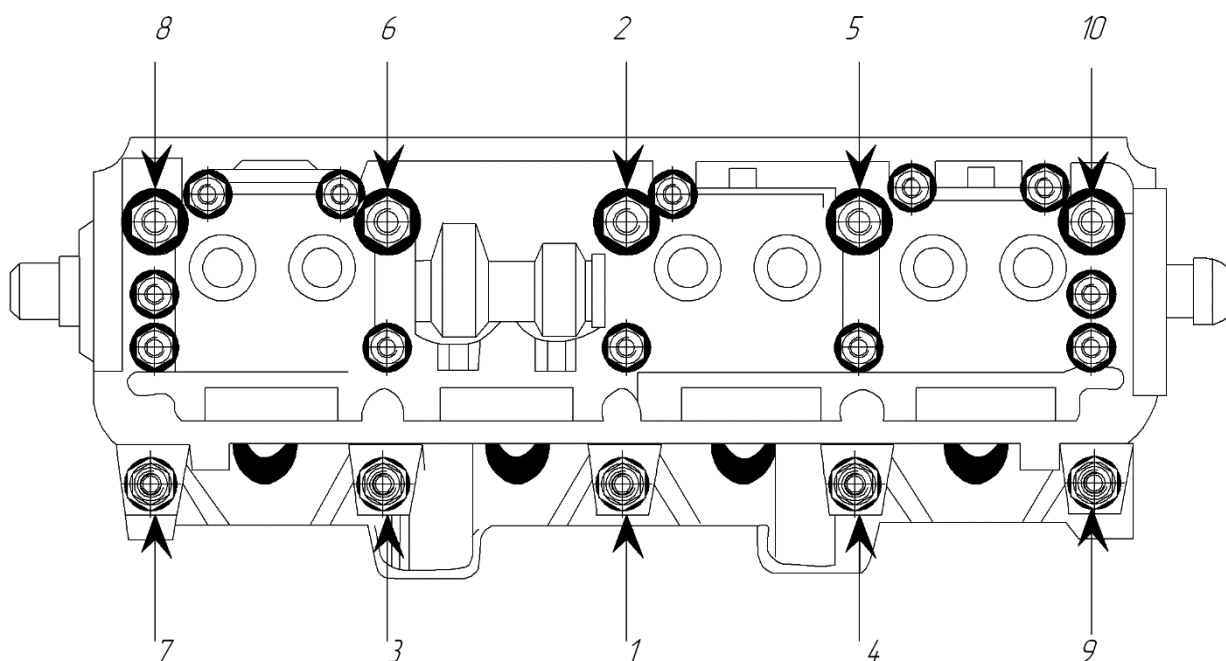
Порядок затягивания болтов крепления головки цилиндров
